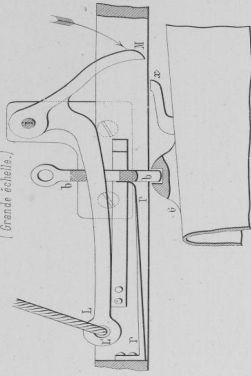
Tube lance-torpille à cuiller construit par M. Farcot.
